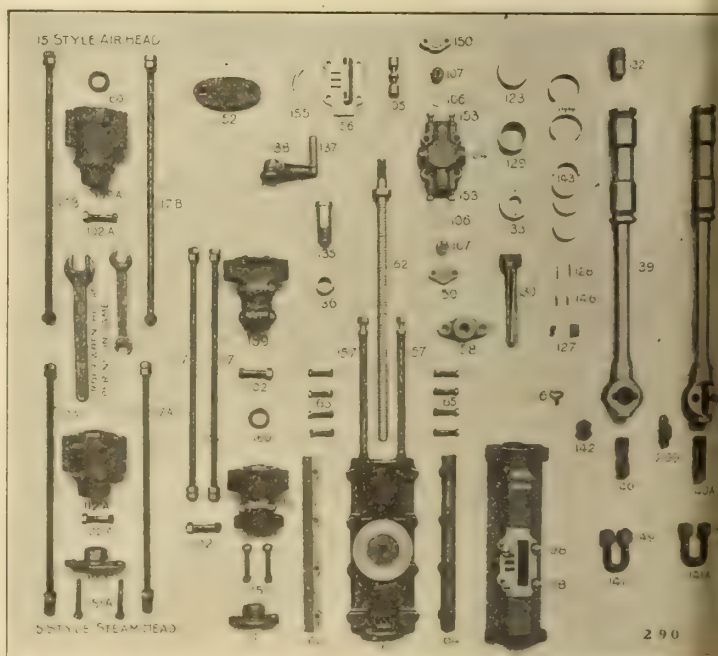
Hauptteile einer Ingersoll-Bohrmaschine.
